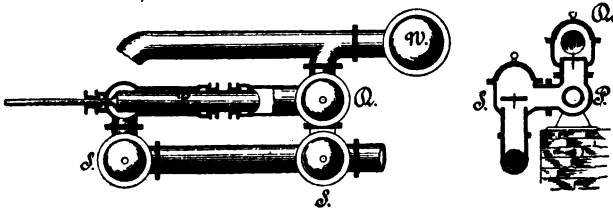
Grundriß, Fig. 191 Schnitt einer Doppelpumpenpumpe.
